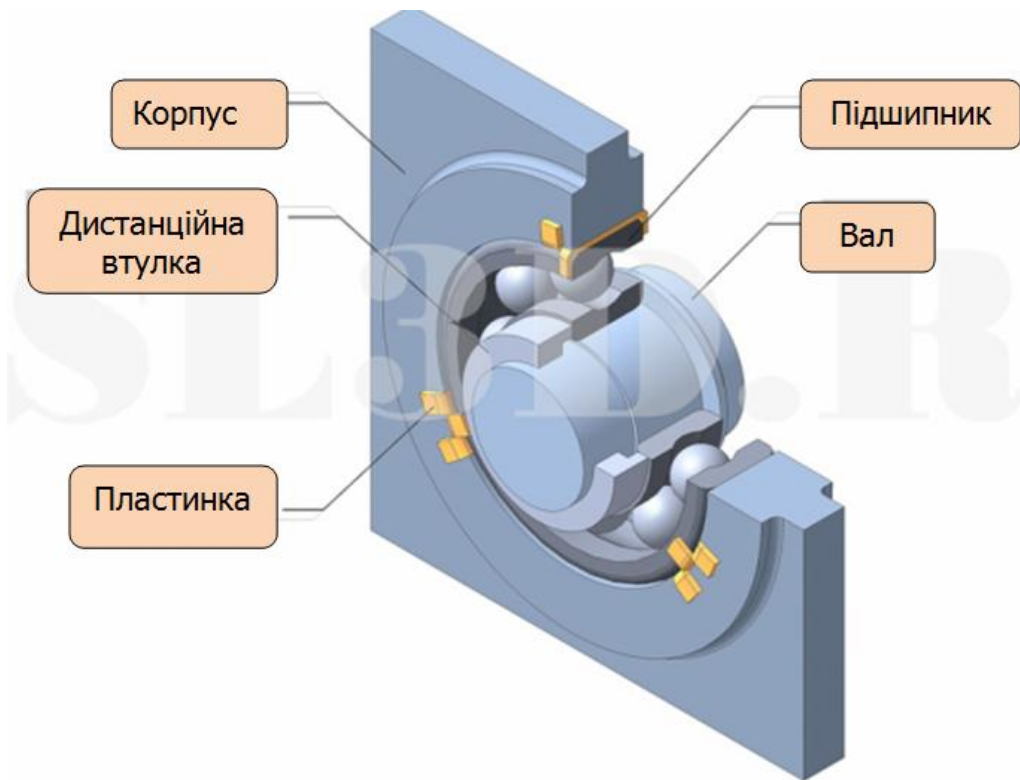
Установка підшипника з допомогою пластинок з розвідними кінцями
